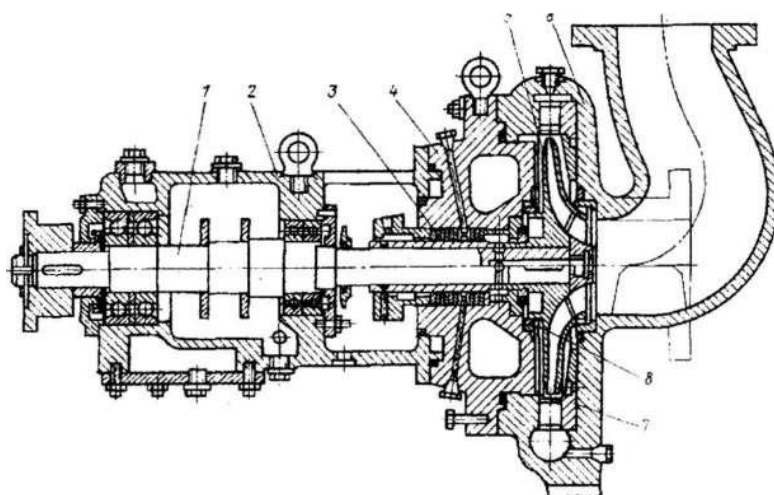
Консольный центробежный насос типа К с направляющим аппаратом: 1 - вал; 2 - подшипниковый кронштейн; 3 - уплотнение; 4 - крышка; 5 - рабочее колесо; 6 - корпус; 7 - направляющий аппарат; 8 - уплотнительное кольцо
